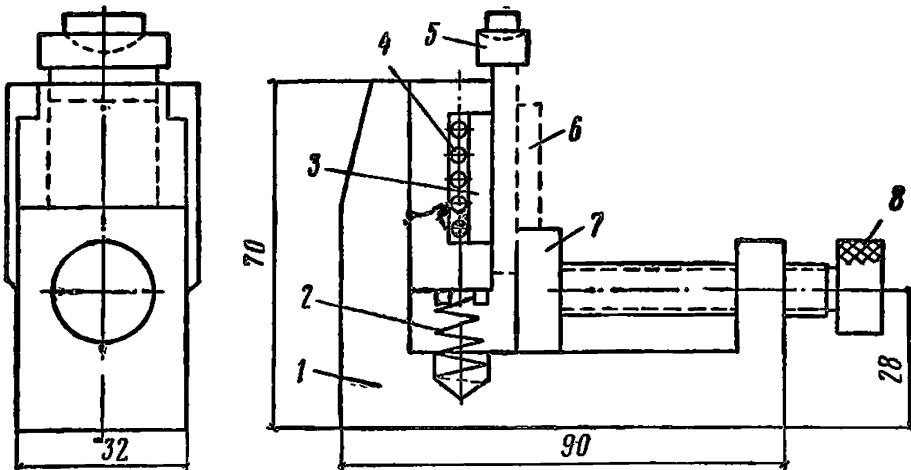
Приспособление для испытания образцов на сдвиг при сжатии
